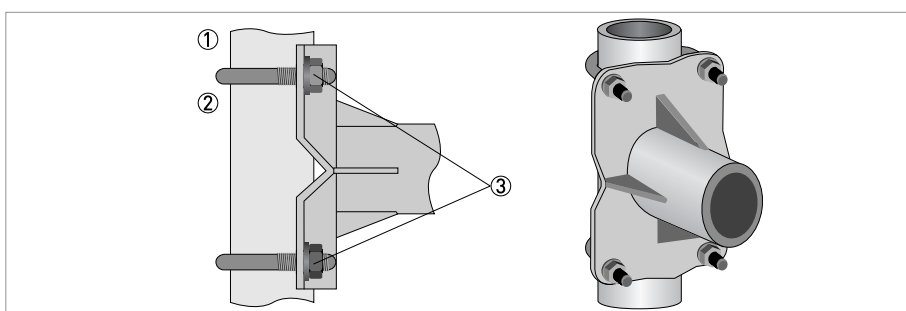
Крепление корпуса преобразователя сигналов полевого исполнения к трубе
